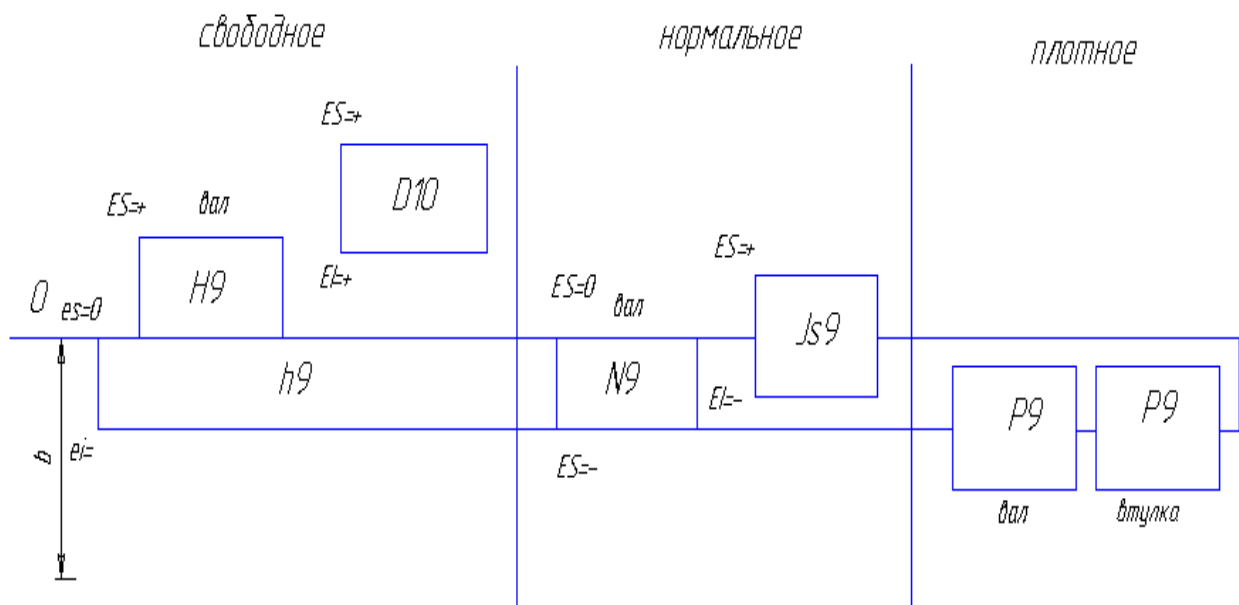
Схема полей допусков для соединения с призматической и клиновидной шпонками ГОСТ 23360 -78 И ГОСТ 24068 – 80
